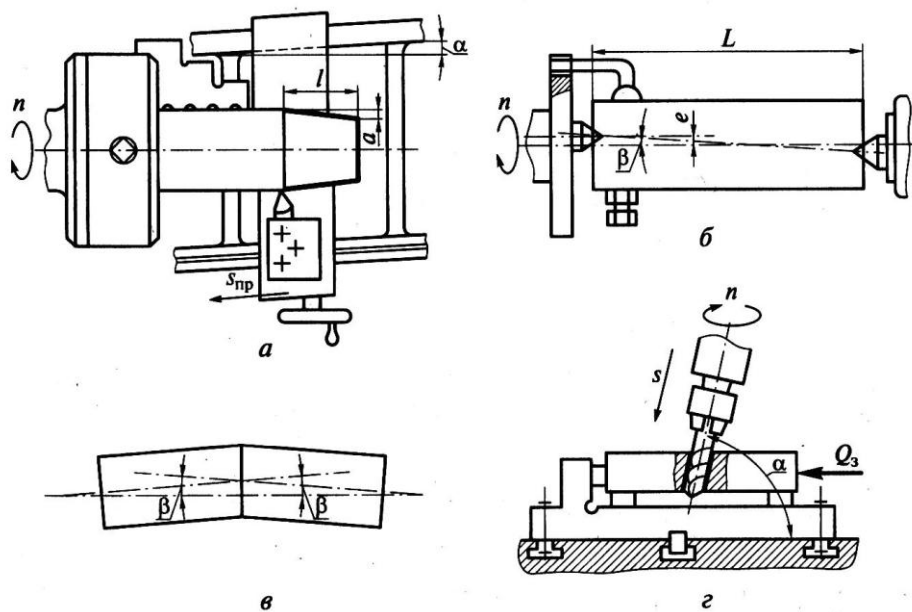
Схема утворення похибок обробки на токарних (а...в) та свердлильному верстаті (г)
